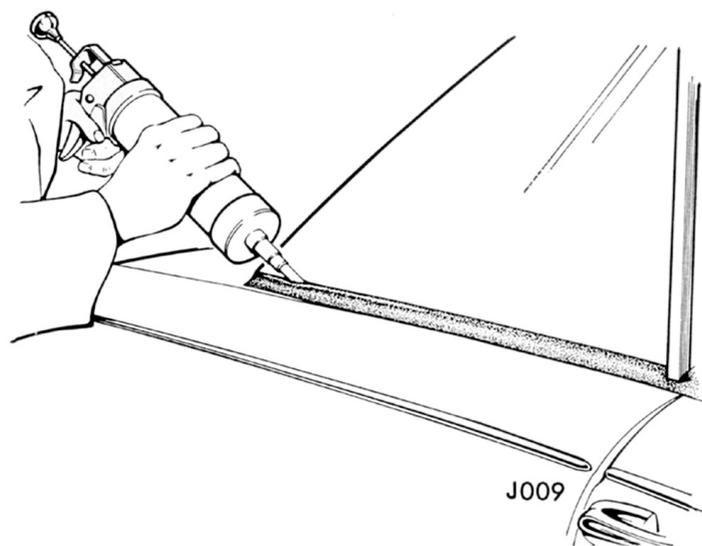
Application du produit d'étanchéité entre la bande d'étanchéité et le panneau de toit
